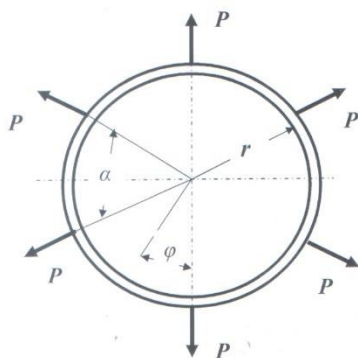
Схема нагружения кольцевой заготовки 6-ю равномерно распределенными радиальными силами
